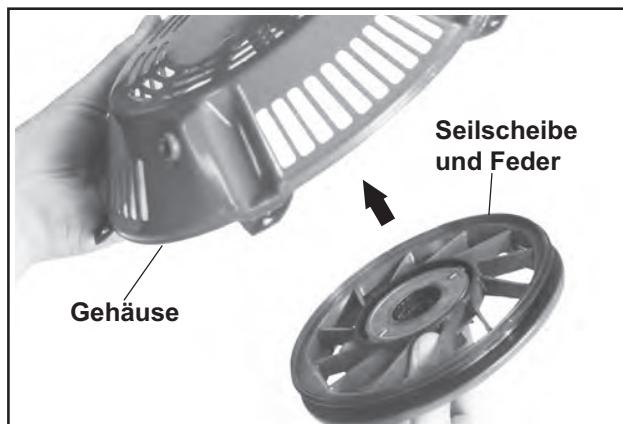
Installation der Seilscheibe und der Feder im Gehäuse.
